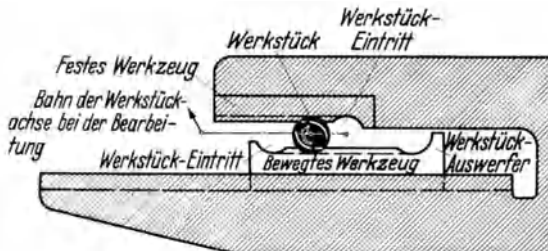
Vorrichtung zum Gewindewalzen. Draufsicht.
